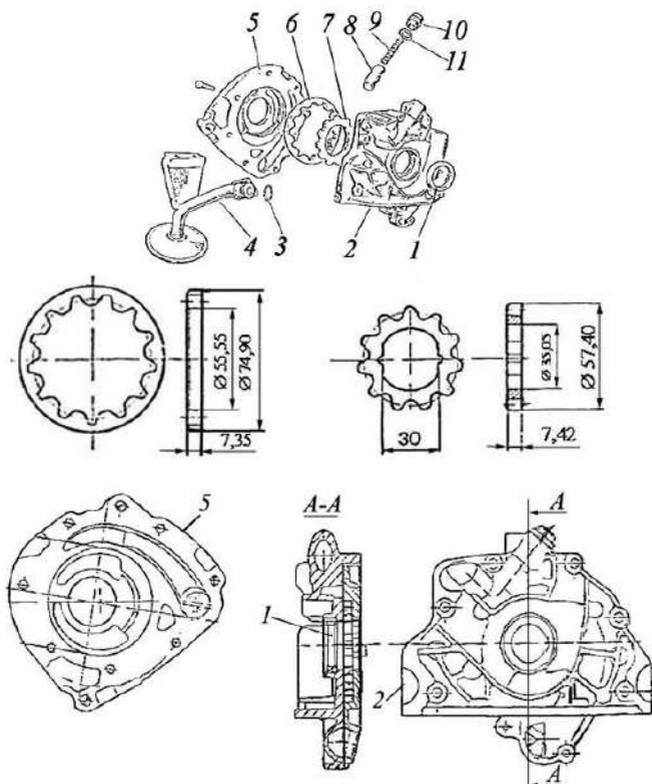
Конструкція масляного насоса з внутрішнім зачепленням шестерень: 1 – кільце; 2, 5 – кришка; 3 – кільце; 4 – заборник; 6 – ведена шестірня; 7 – ведуча шестірня; 8 – золотник клапана; 9 – пружина; 10 – упор; 11 – шайба
